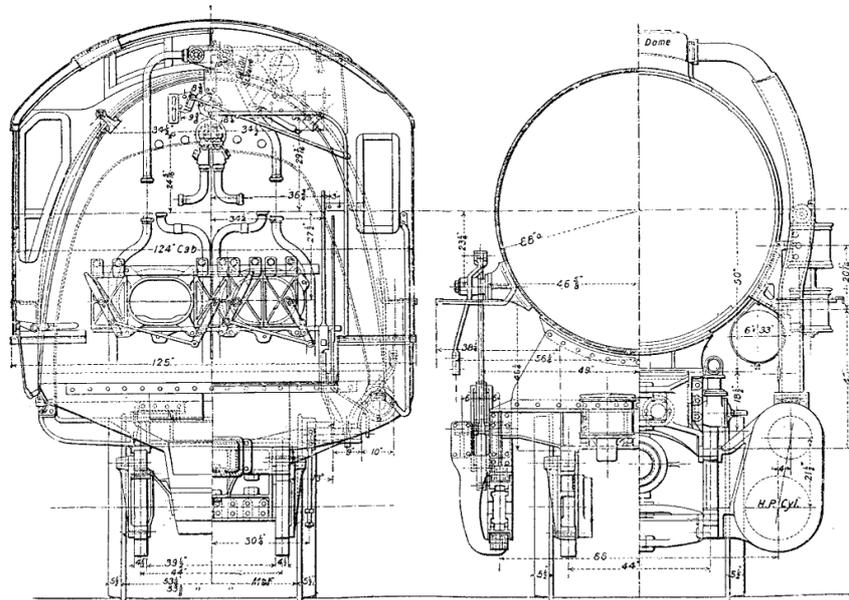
Locomotive Mallet. Vues d'arrière, coupes verticales par le support des glissières d'arrière et en avant des petits cylindres.
